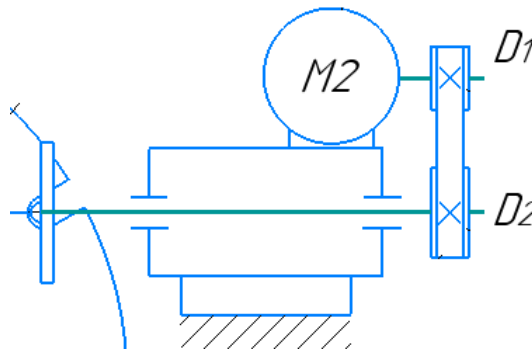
Кінематична схема силової головки для фрезерування пазу
